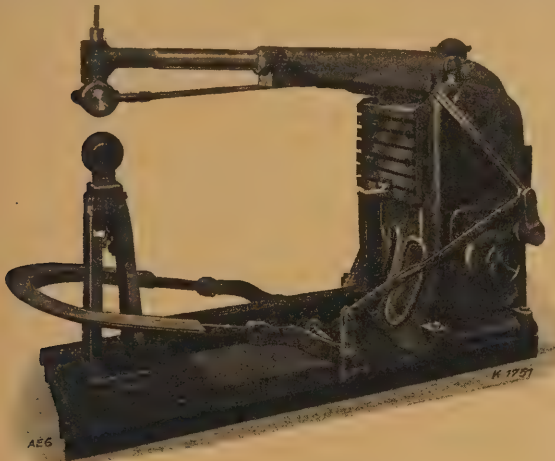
Längsnahtschweißmaschine zum Verschweißen von Bekleidungsblechen, Karosserieteilen und dergl. Ausladung 1200 mm; Leistung 30 kVA.
